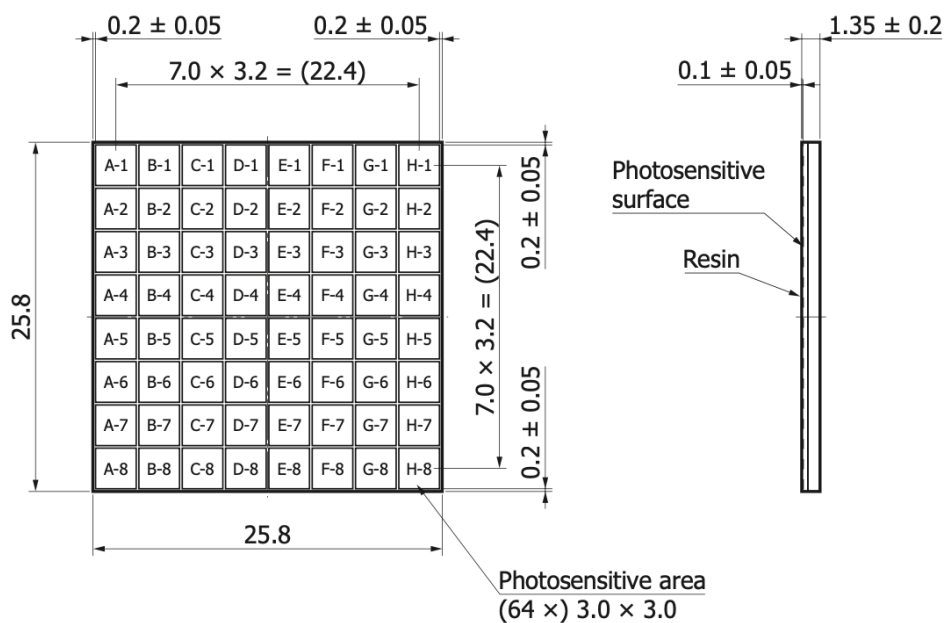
Чертеж матрицы SiPM Hamamatsu S13361-3050AE-08 с габаритными размерами
